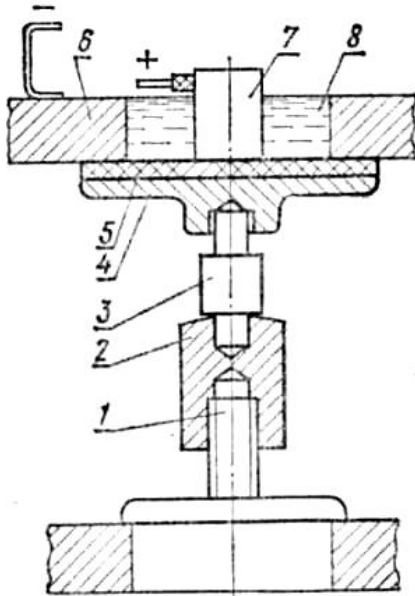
Відновлення поверхні посадочного отворів в корпусі коробки передач: 1 - гвинт з фланцем; 2 - гайка, 3 - упорний стрижень, 4 - диск, 5 - ізоляційна (гумова) прокладка; б - корпус коробки передач (катод); 7 - анод, 8 - ванна в відновлюваному отворі
